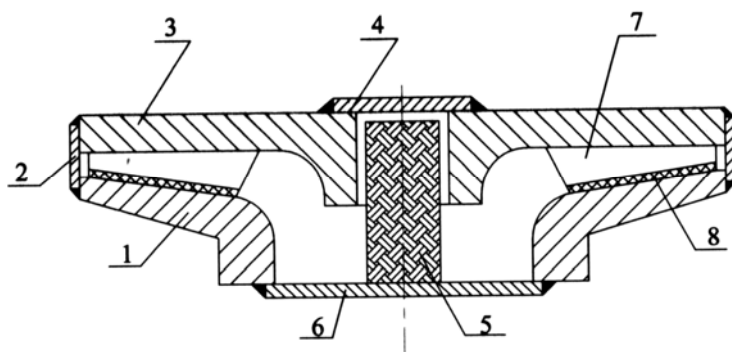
Схема автовакуумного паяння робочого колеса:
